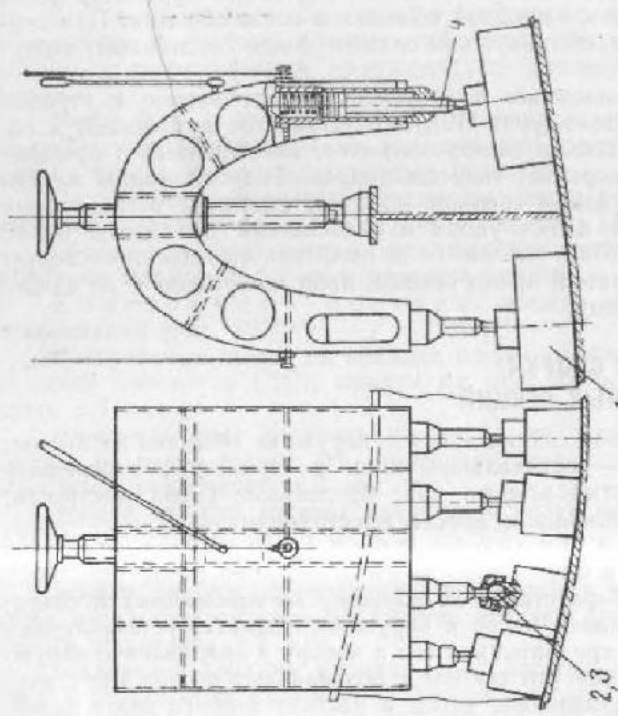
Магнитогидровлическое устройство для механизации прижатия набора к наружной обшивке. 1 — электромагниты; 2 и 3 — сферические шарниры; 4 — поршни гидроцилиндра.
